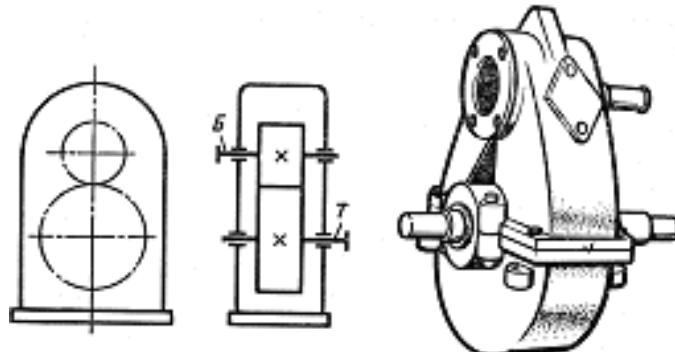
Двухступенчатый цилиндрический редуктор вертикальный
